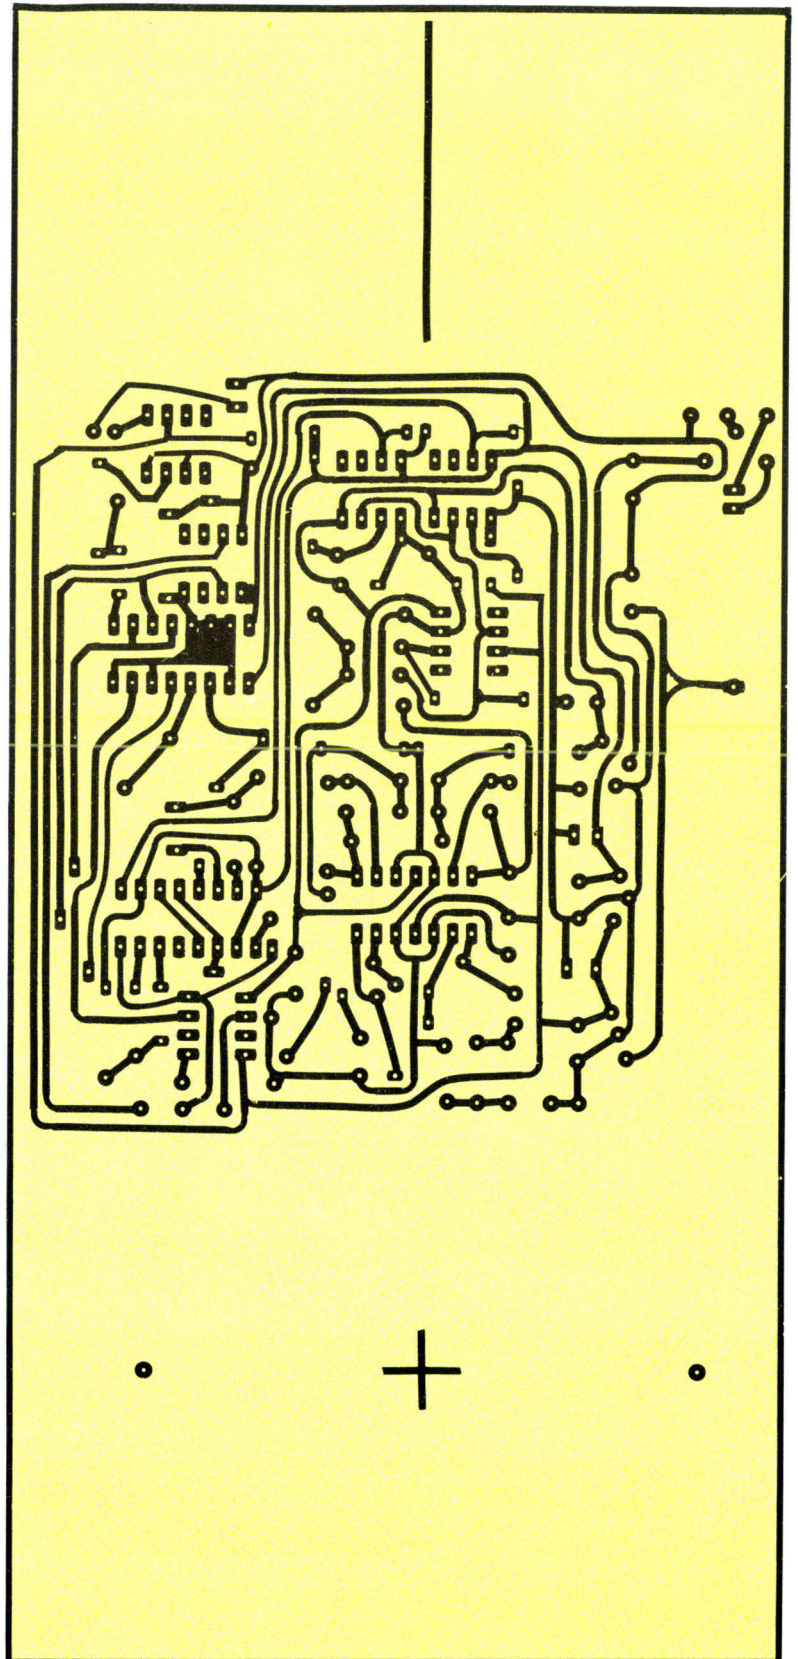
Circuit imprimé vu côté «soudures» (éch. 1).
